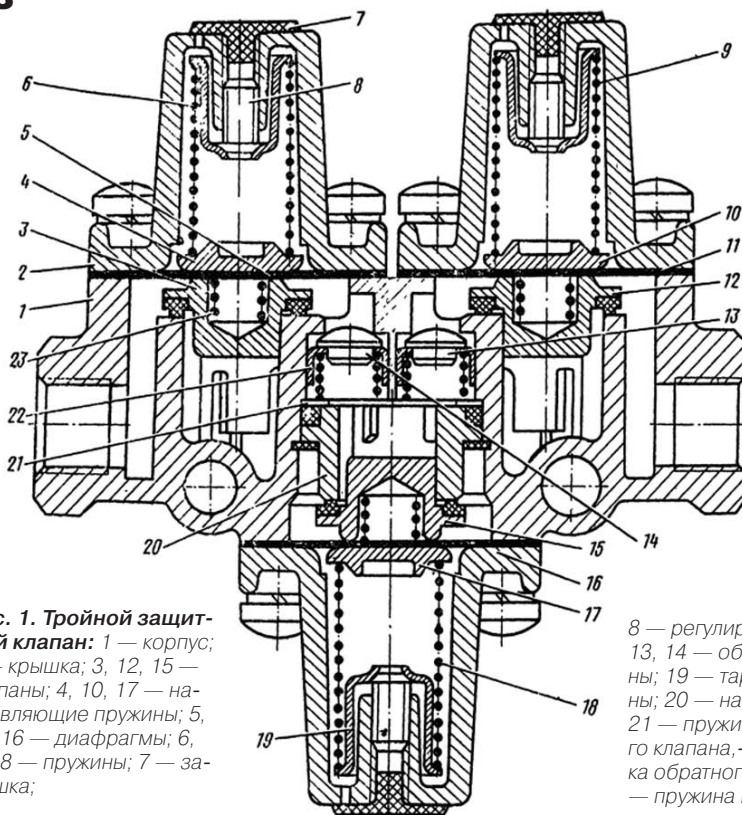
Тройной защитный клапан: 1 — корпус; 2 — крышка; 3, 12, 15 — клапаны; 4, 10, 17 — направляющие пружины; 5, 11, 16 — диафрагмы; 6, 9, 18 — пружины; 7 — заглушка;
